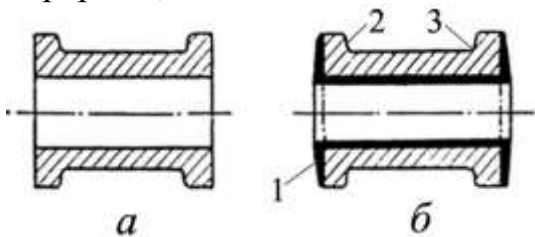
Конструювання виливка (б) на основі кресленика готової деталі (а):
